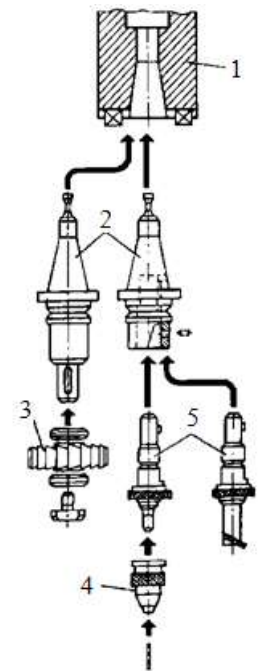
Інструментальний комплект для БЦ верстату: 1 – шпиндель; 2 – оправки; 3 – фреза; 4 – патрон для затиску свердла; 5 – перехідні оправки.
